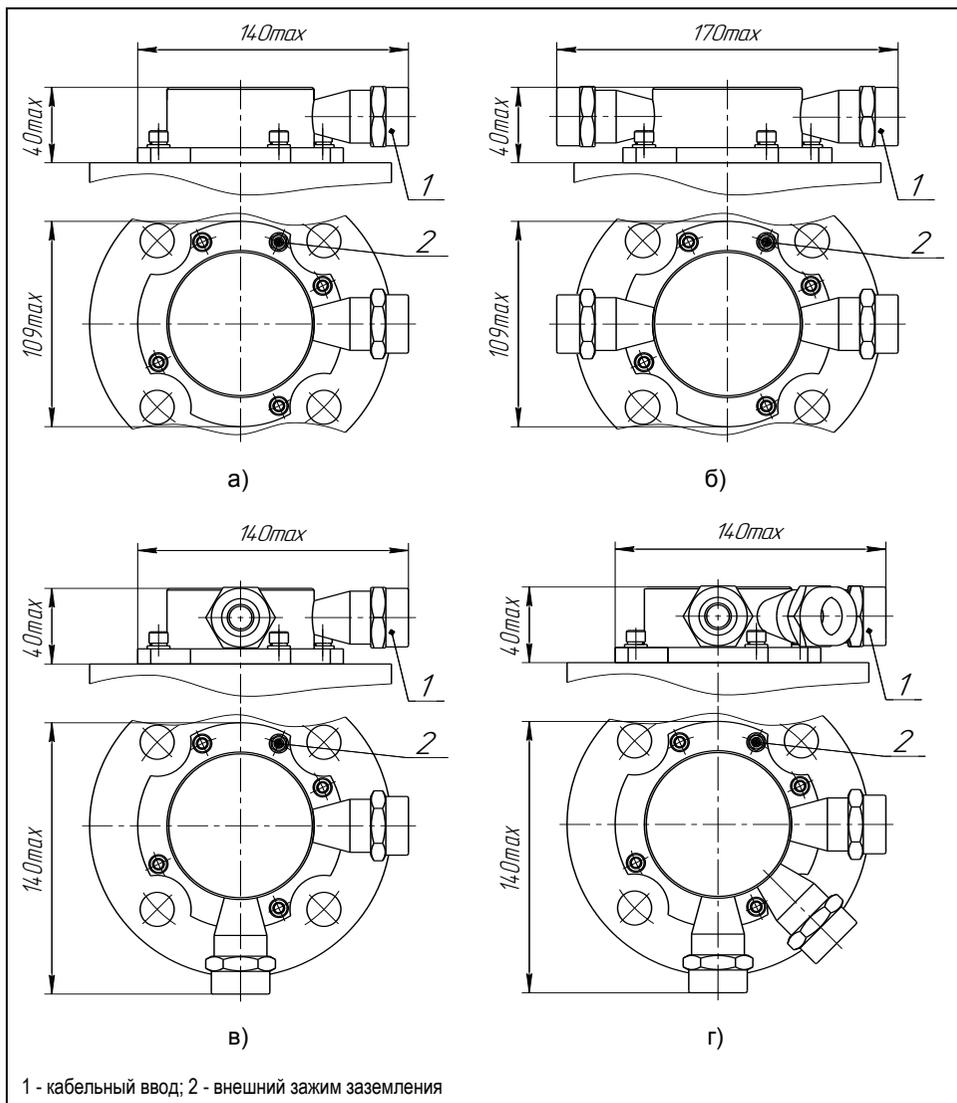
Варианты исполнения корпуса из нержавеющей стали:
